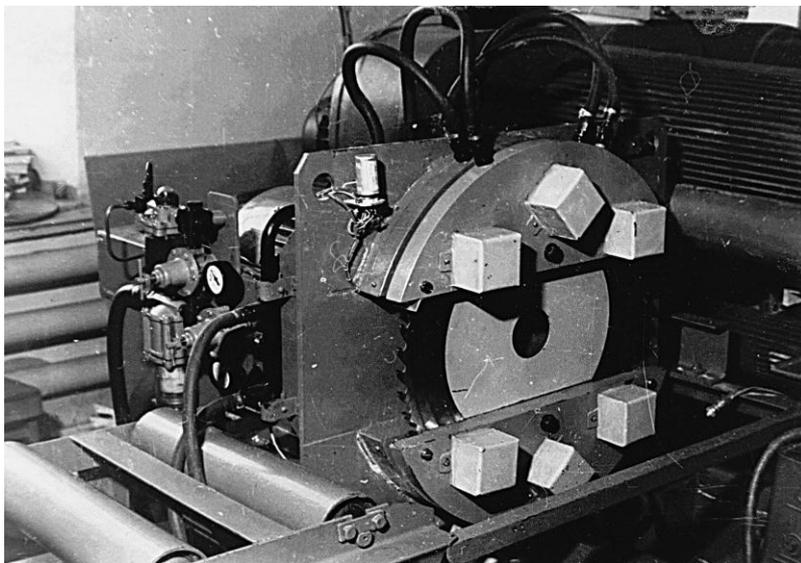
Общий вид круглопильного станка с кольцевой пилой
